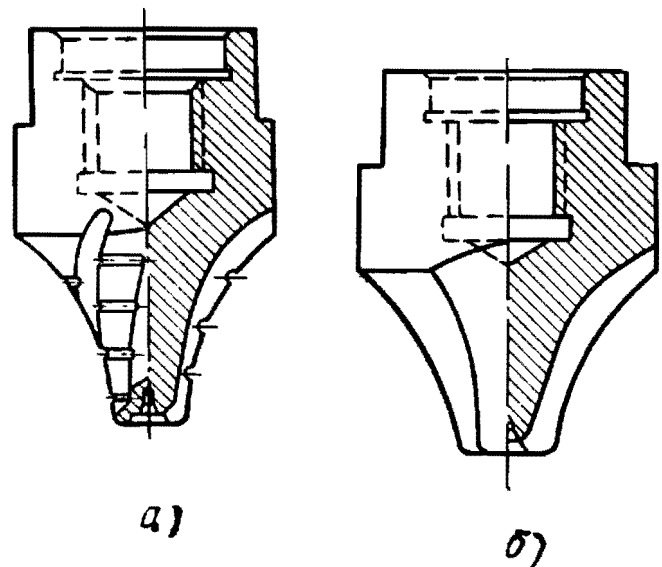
Пальцевые модульные фрезы: а — для черновой обработки, б — для чистовой обработки
